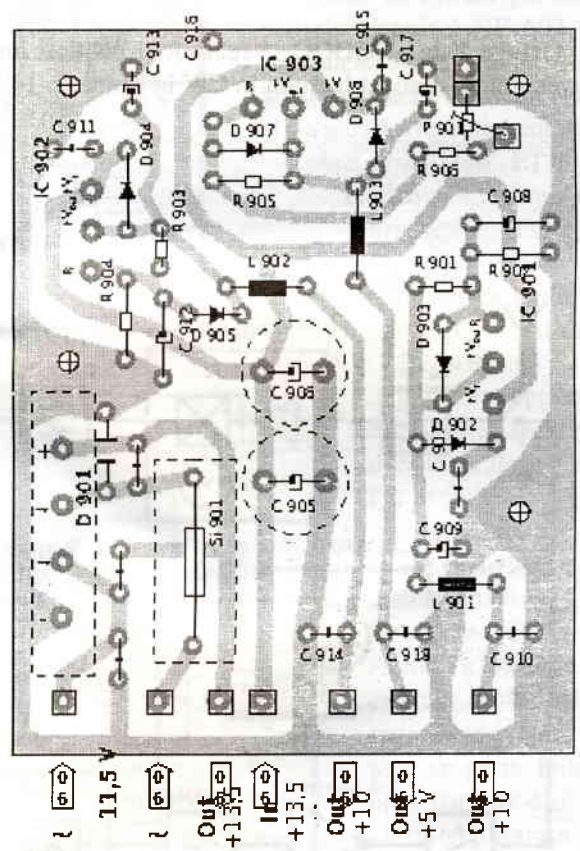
Placa de circuit imprimat 900; dispunerea componentelor (vedere dinspre fața superioară)
